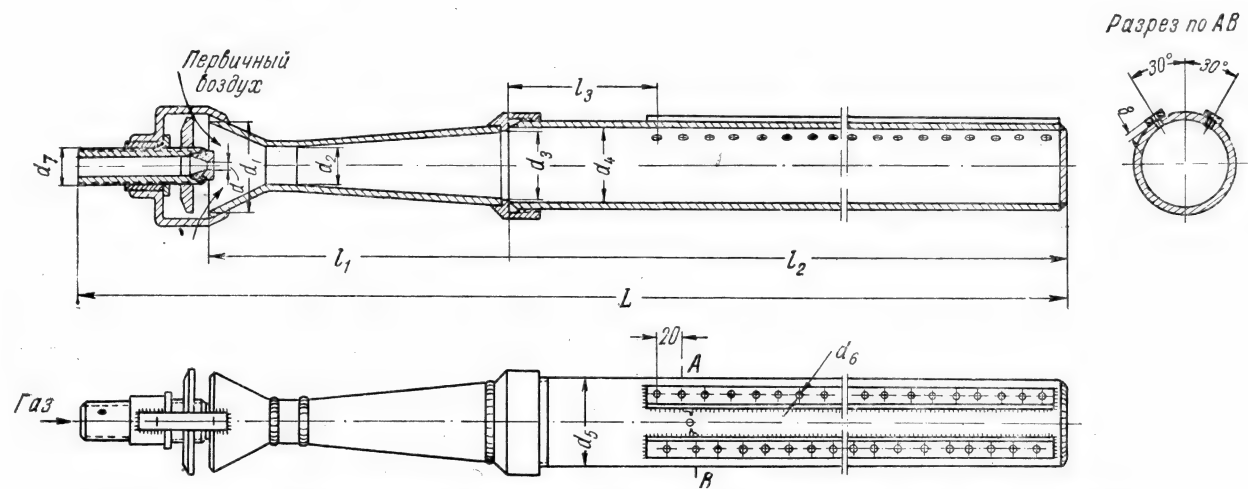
Газовая инжекционная горелка низкого давления сварной конструкции.
